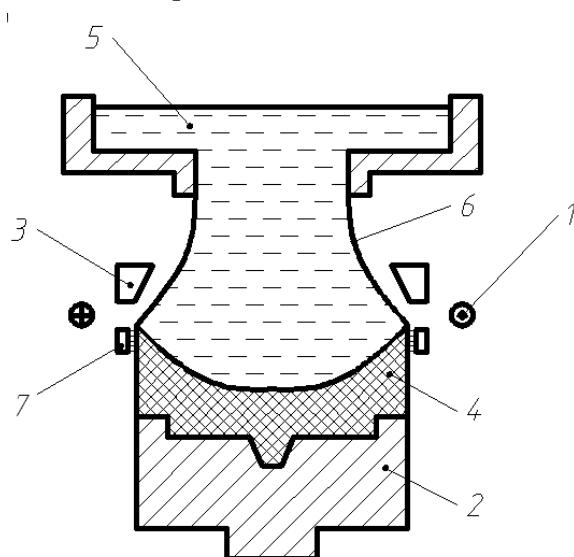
Установка для литья слитков металла: 1 – обмотка индуктора, 2 – литейный стол, 3 – электромагнитный экран, 4 – металл в твердом состоянии (слиток), 5 – металл в жидком состоянии, 6 – свободная поверхность металла, 7 – охладитель
